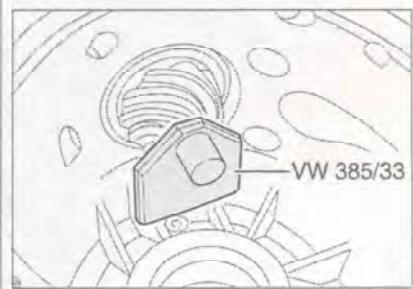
Установите приспособление VW 385/33 на ведущую шестерню.
